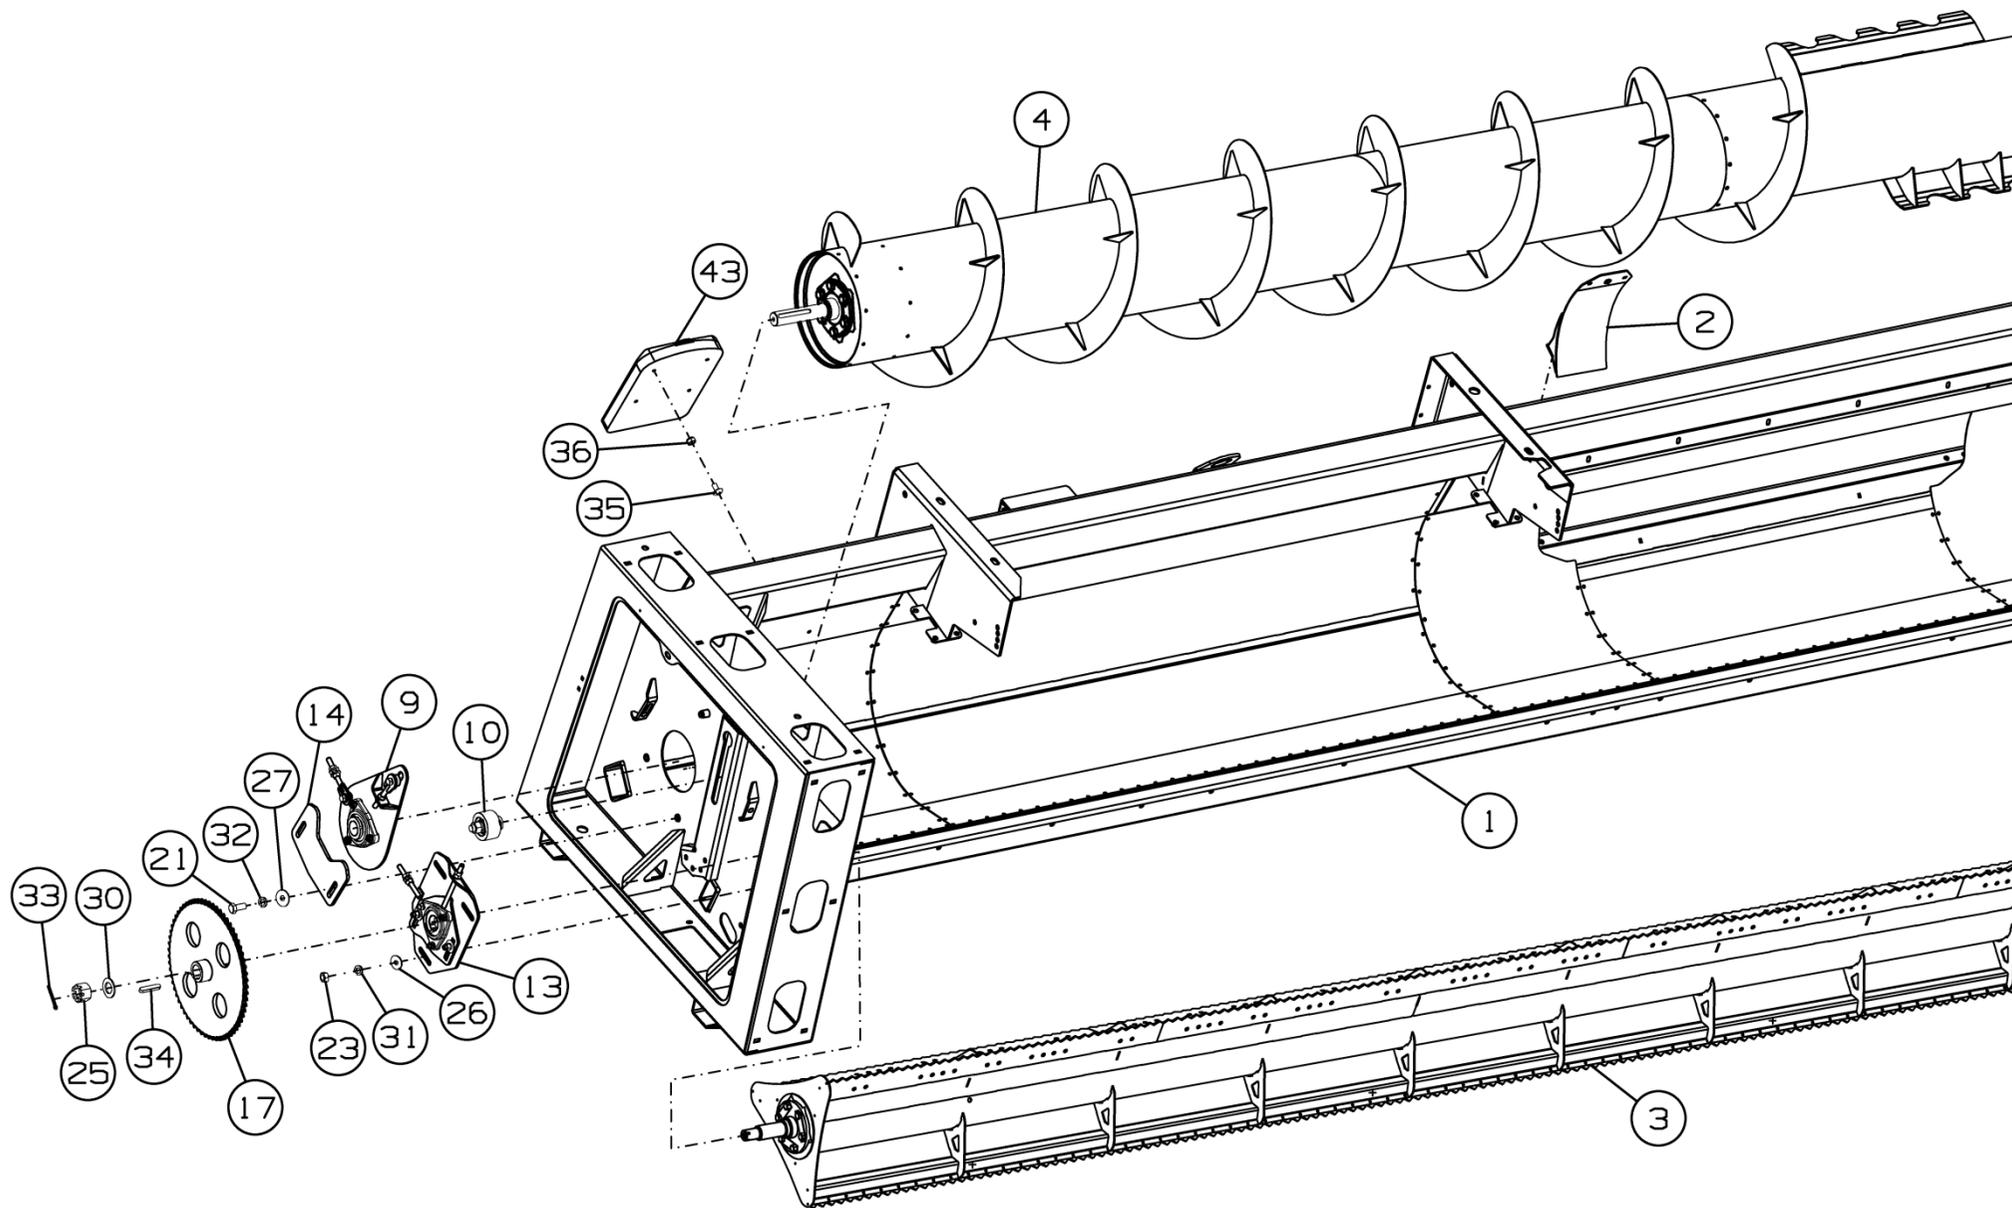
Корпус жатки SS-780.01.01.000У-04
